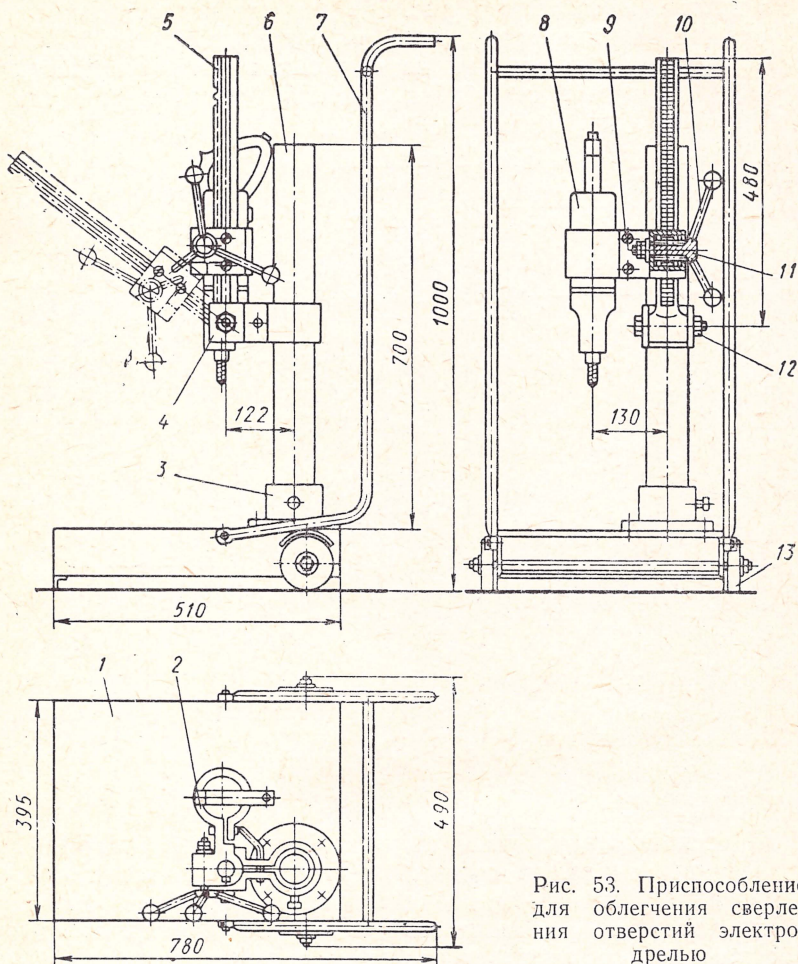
Приспособление для облегчения сверления отверстий электродрелью
